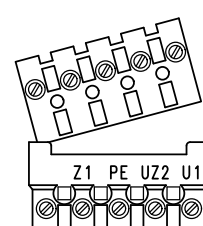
Motorstecker für 3 x 500V / 400V / 230V
